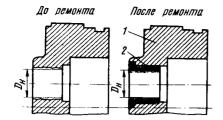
Схема восстановления размера отверстия в корпусе масляного насоса: 1 — корпус масляного насоса; 2 — ремонтная деталь (втулка)
